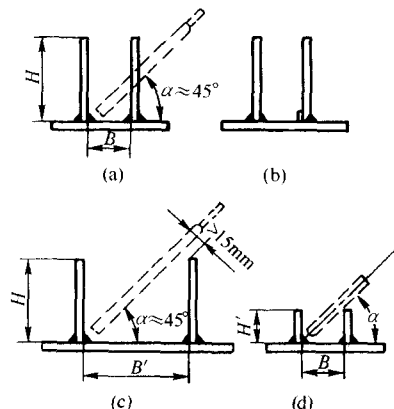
焊条电弧焊接时的操作空间
